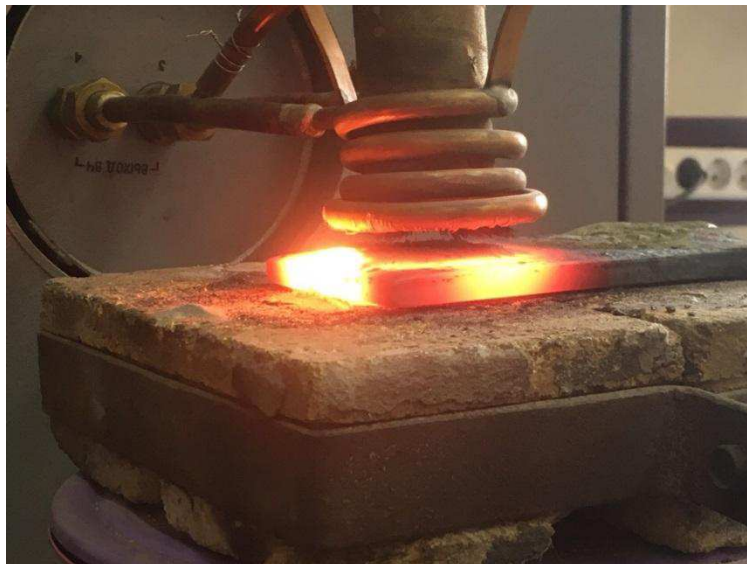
Процесс наплавки порошка H73X16C3P3
